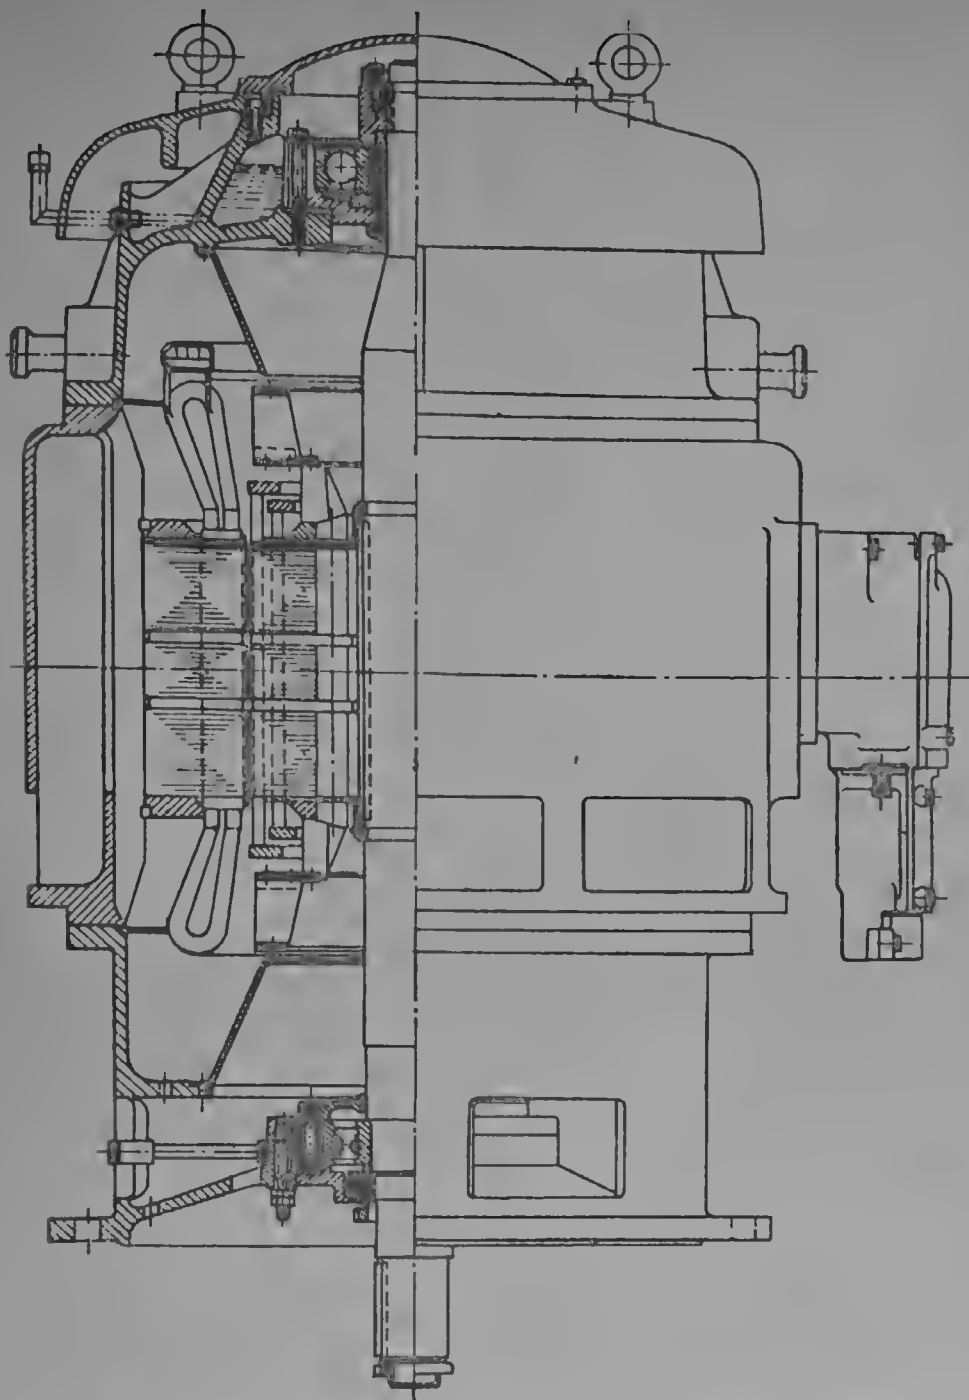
Вертикальный асинхронный двигатель с фланцевым креплением
